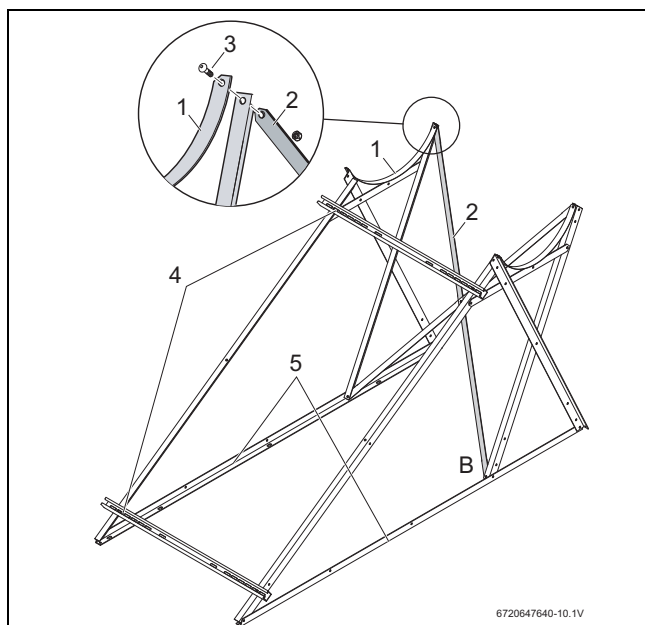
Atornillar los perfiles de cubierta plana/tejado inclinado
